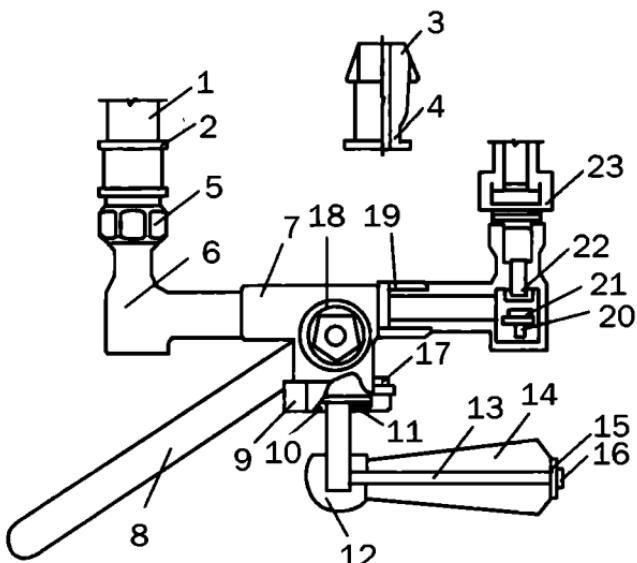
Конструкция смесителя с переключателем пробкового типа: 1 — труба; 2 — муфта; 3 — уплотнение втулки; 4 — эксцентрическая втулка; 5, 9 — накидная гайка; 6 — боковина; 7 — корпус; 8 — излив; 10, 15 — шайба; 11 — ограничитель; 12 — остав; 13 — ось; 14 — рукоятка; 16 — винт; 17 — стопорный винт; 18 — пробка; 19 — уплотнение; 20 — клапан; 21, 23 — прокладка; 22 — втулка
